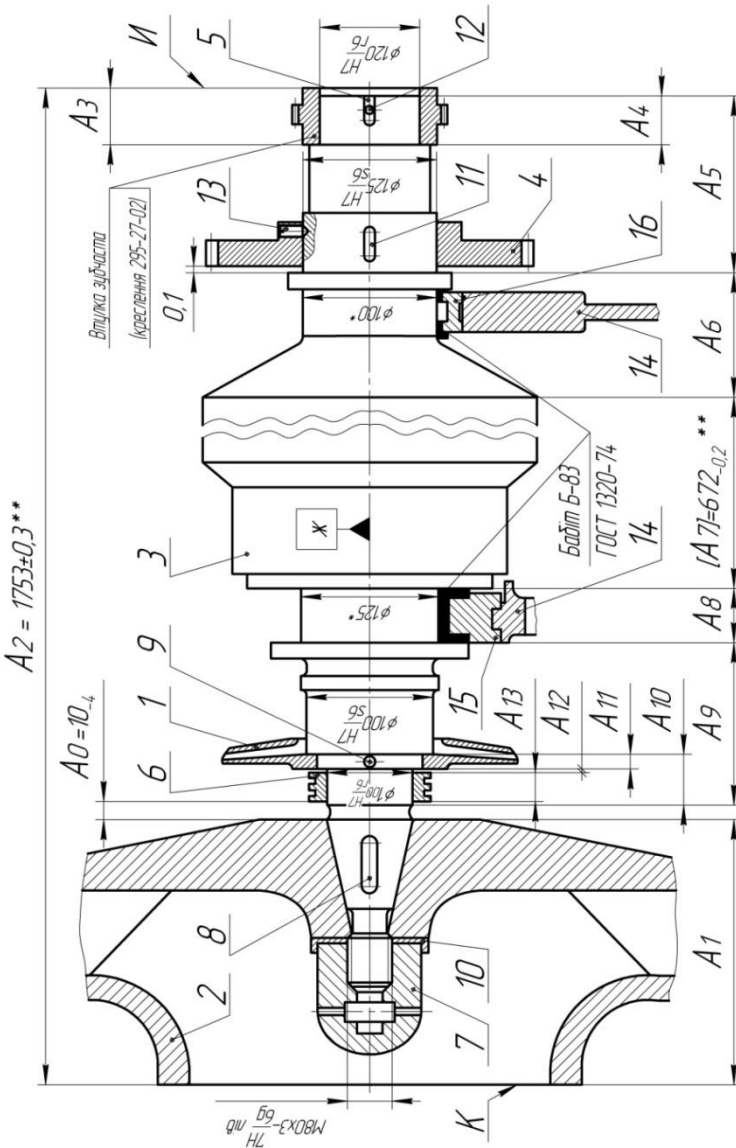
Схематизоване креслення ротора 398Н-25СБ та його РЛ
